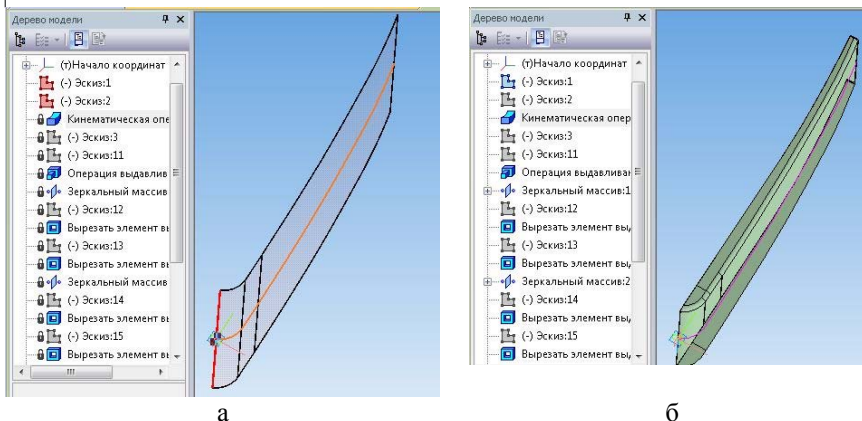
Кінематична операція: а – ескіз; б – деталь
